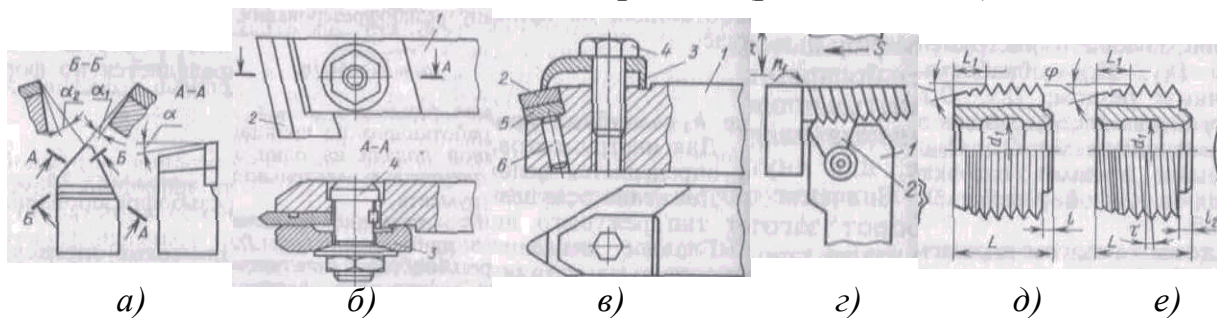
Резьбовые резцы: а – с напаянной твердосплавной пластинкой; б – с призматической вставкой; в – с неперетачиваемой твердосплавной пластинкой; г – многопрофильный; д – круглый с кольцевой нарезкой; е – круглый с винтовой нарезкой
